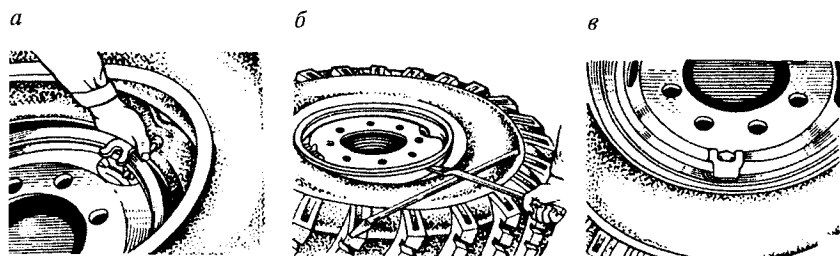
Монтаж колеса с шиной с регулируемым давлением
